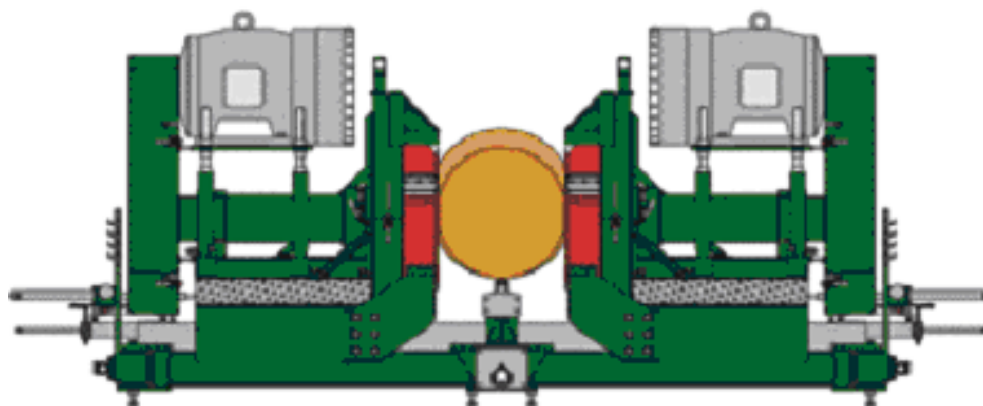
Принцип работы фрезерно-брусующего оборудования
